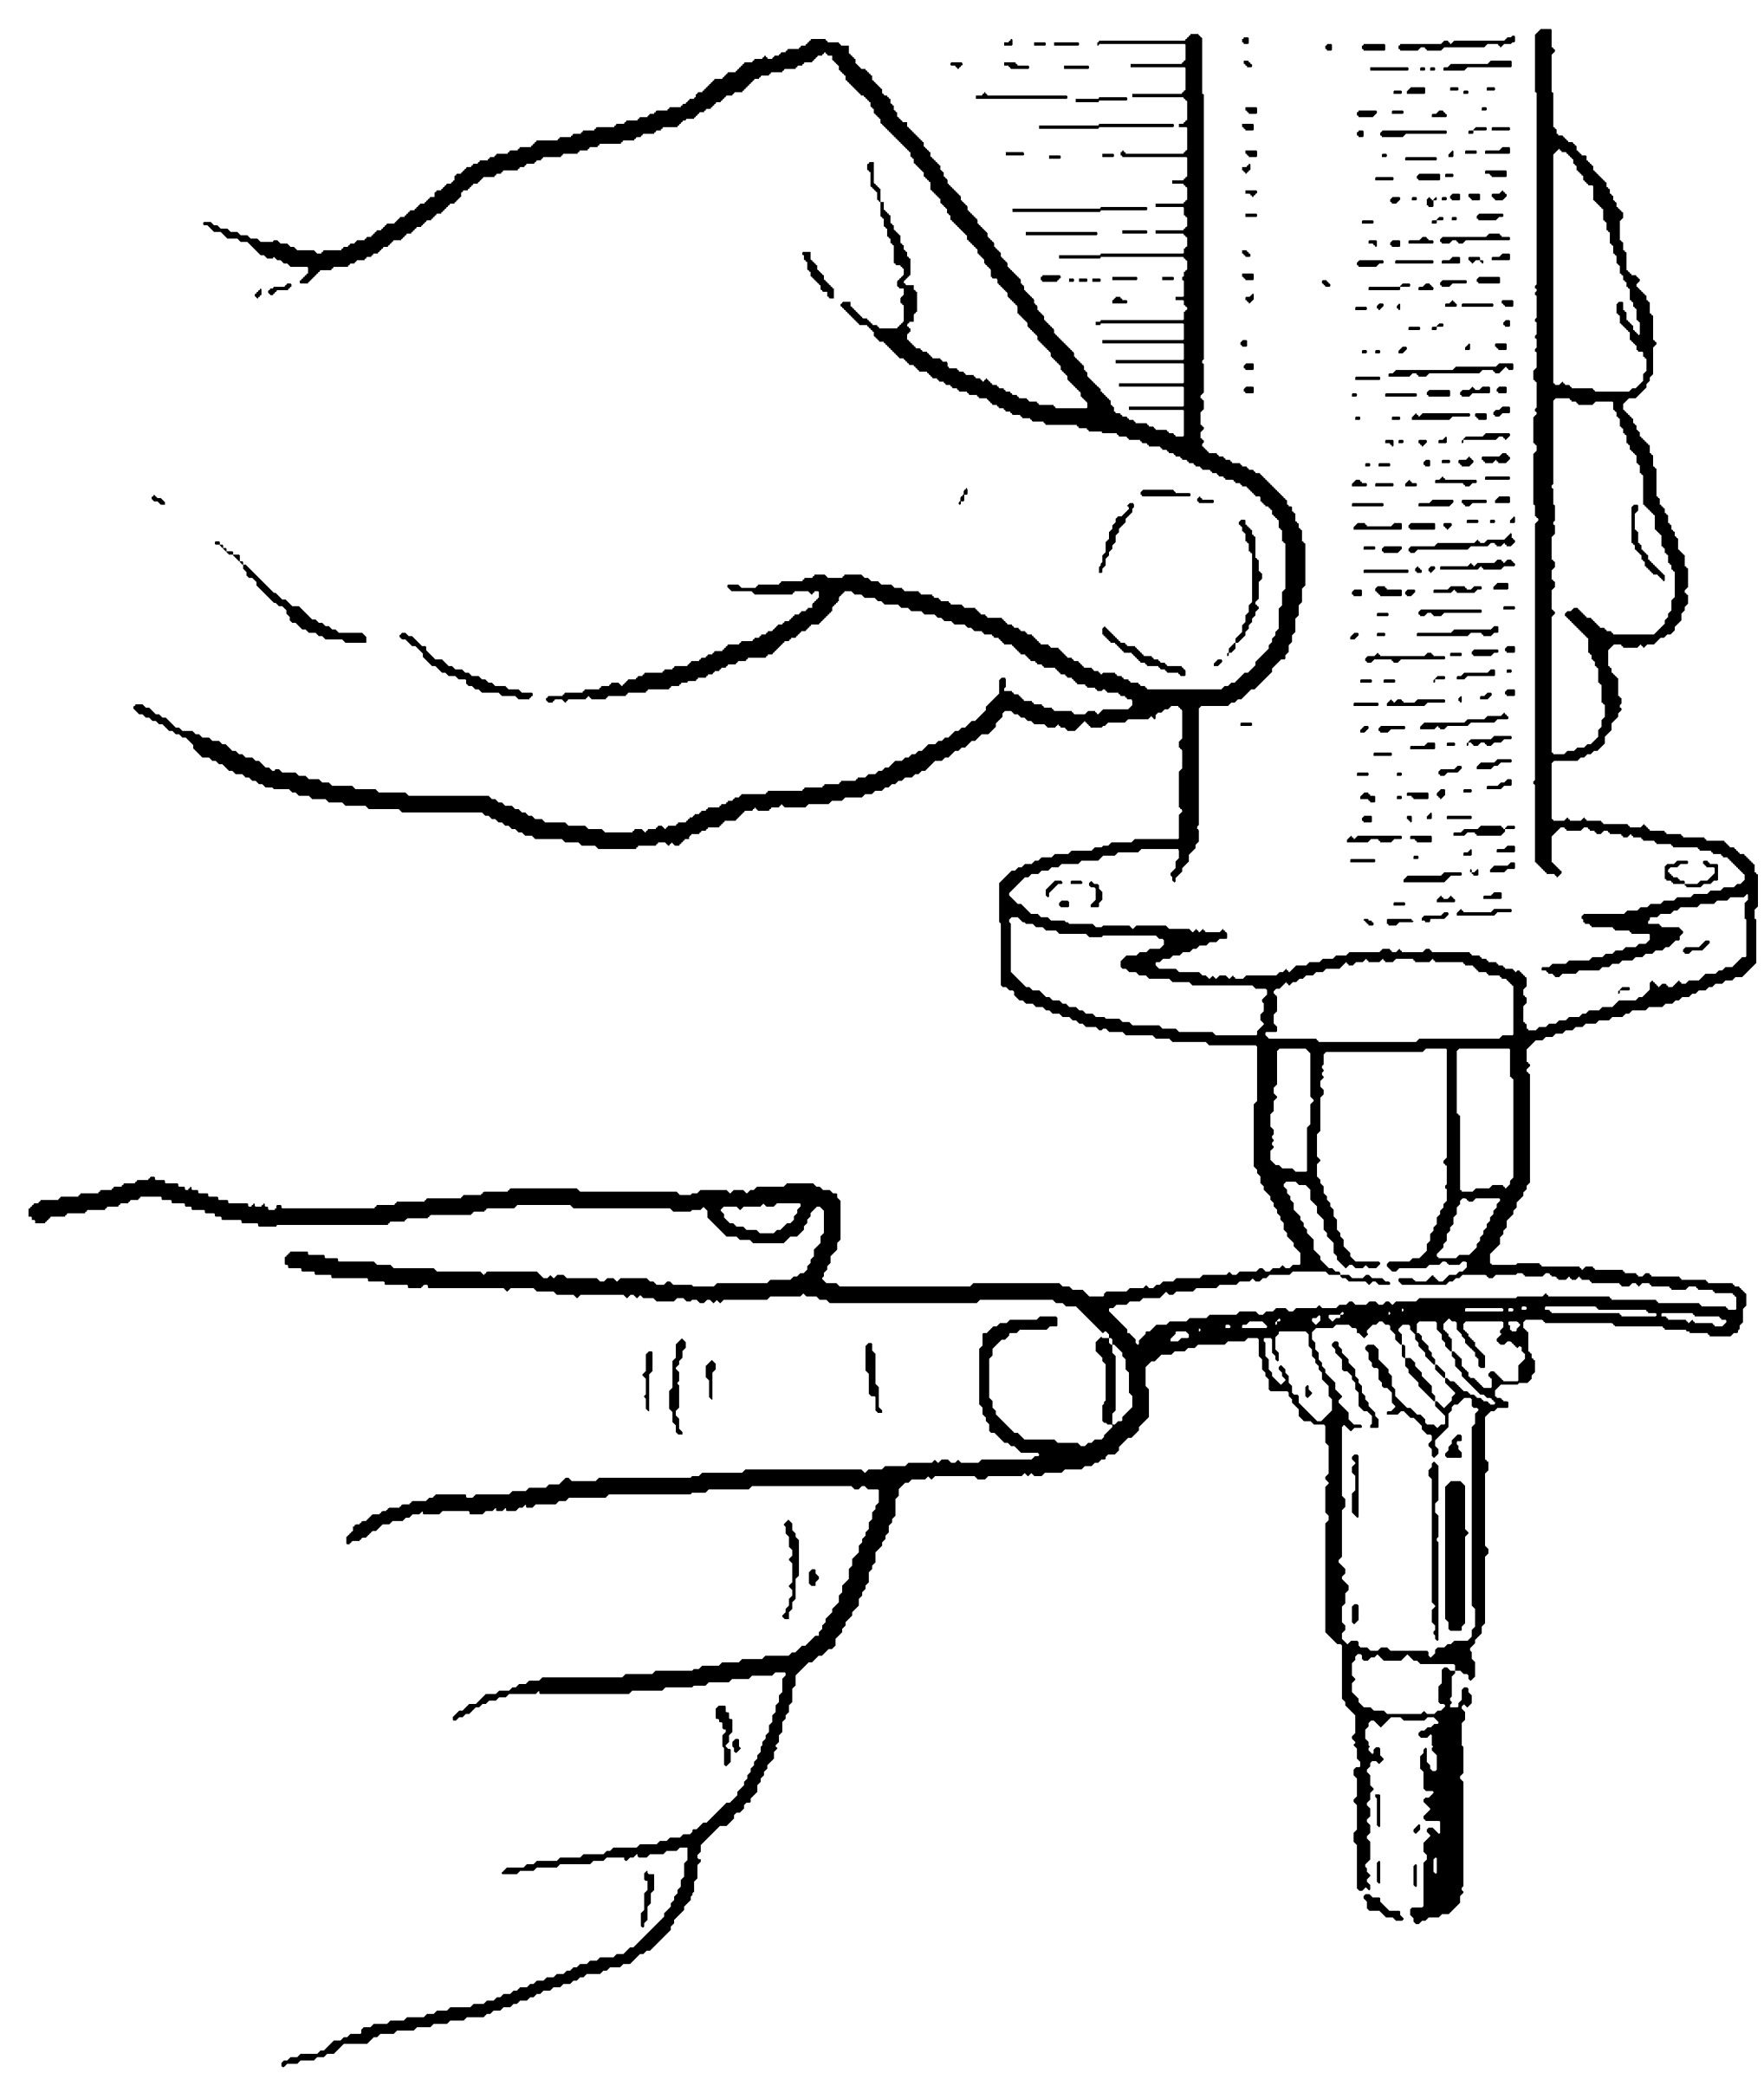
Проверка осевого зазора между корпусом привода масляного насоса и датчиком-распределителем зажигания с шестерней
